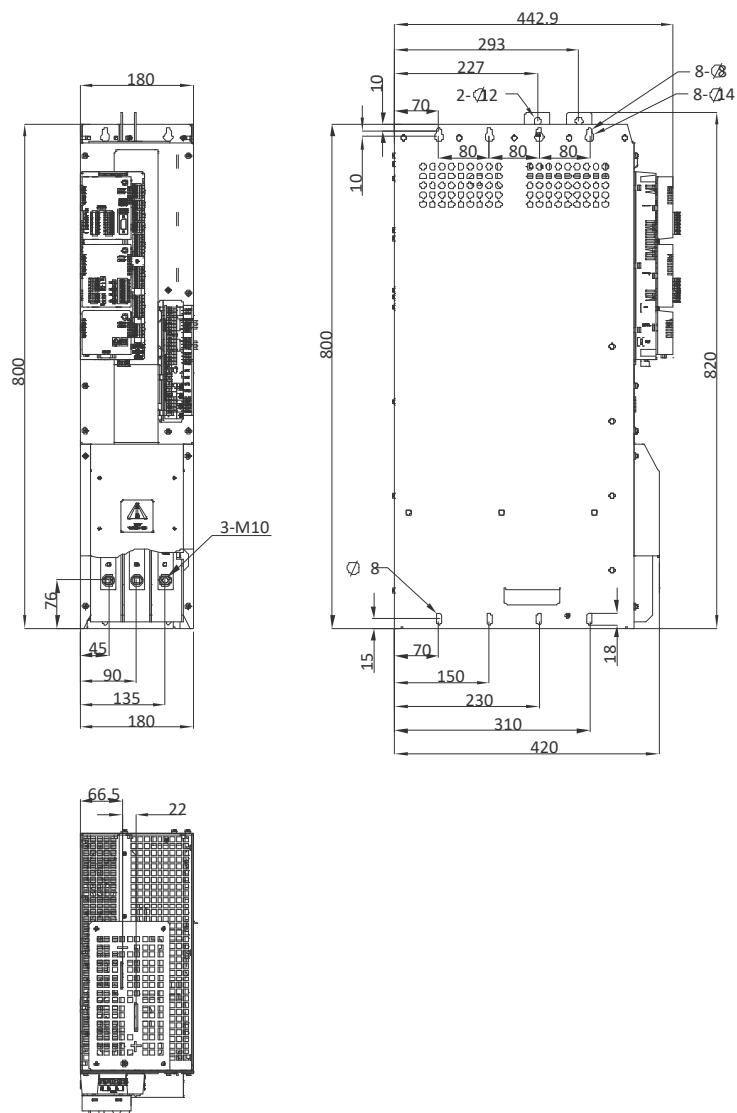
Габаритные размеры инвертора корпуса FR6 (мм)
